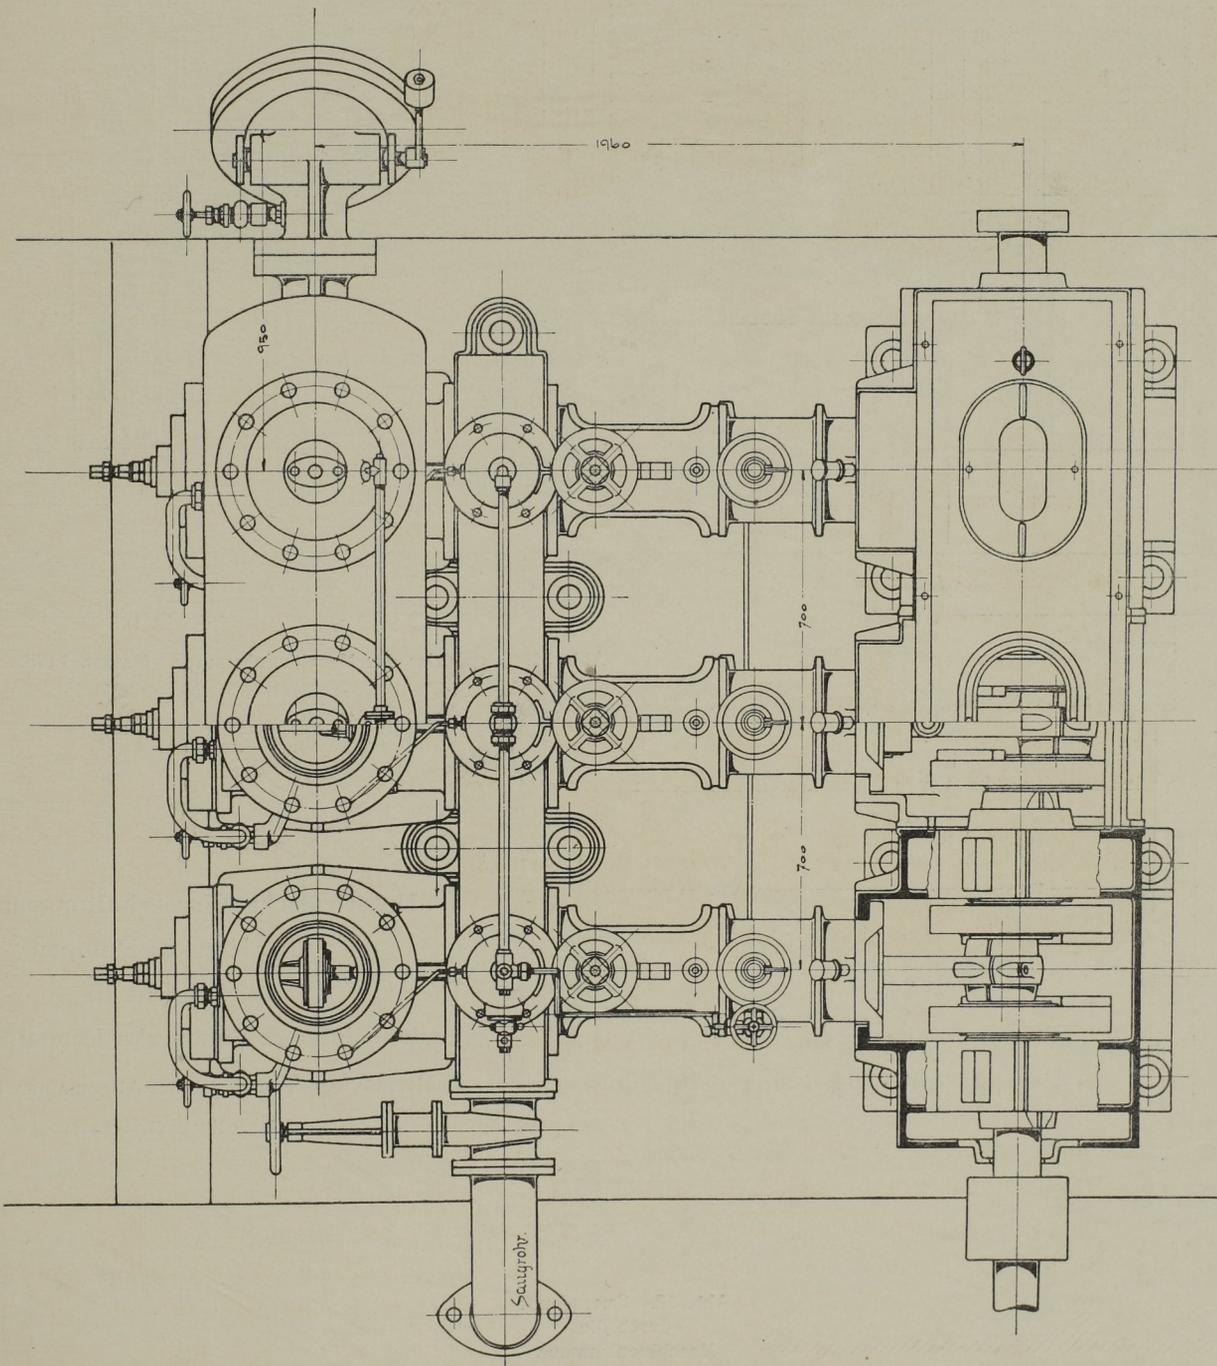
Grundriss der „Express-Pumpe“. Masst. 1:20.
